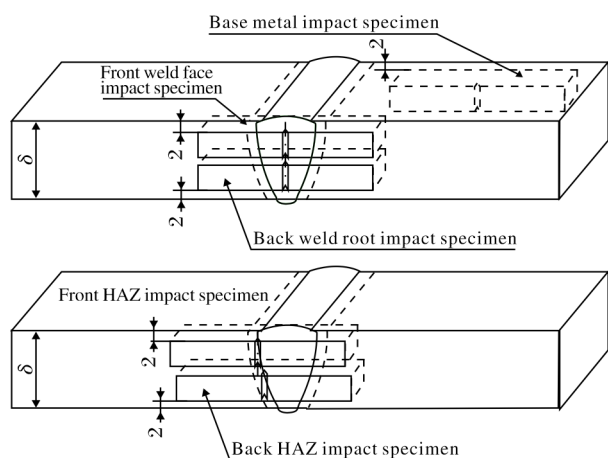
K-TIG 焊接试板焊缝及 HAZ 冲击试样取样示意图
